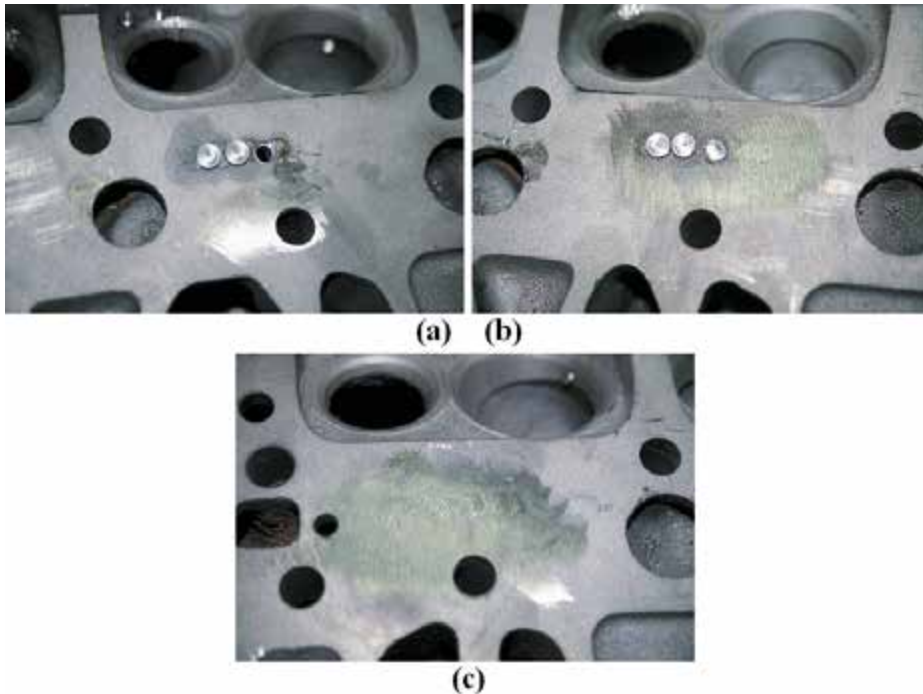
(а) Отверстие для резьбовой пробки готовится с помощью сверла, развертки и метчика. (б) в подготовленные отверстия вворачиваются резьбовые пробки. (с) После зачеканки выступающие части резьбовых пробок зашлифовываются вровень с ремонтируемой поверхностью; источник: *Pearson Education, Inc.
